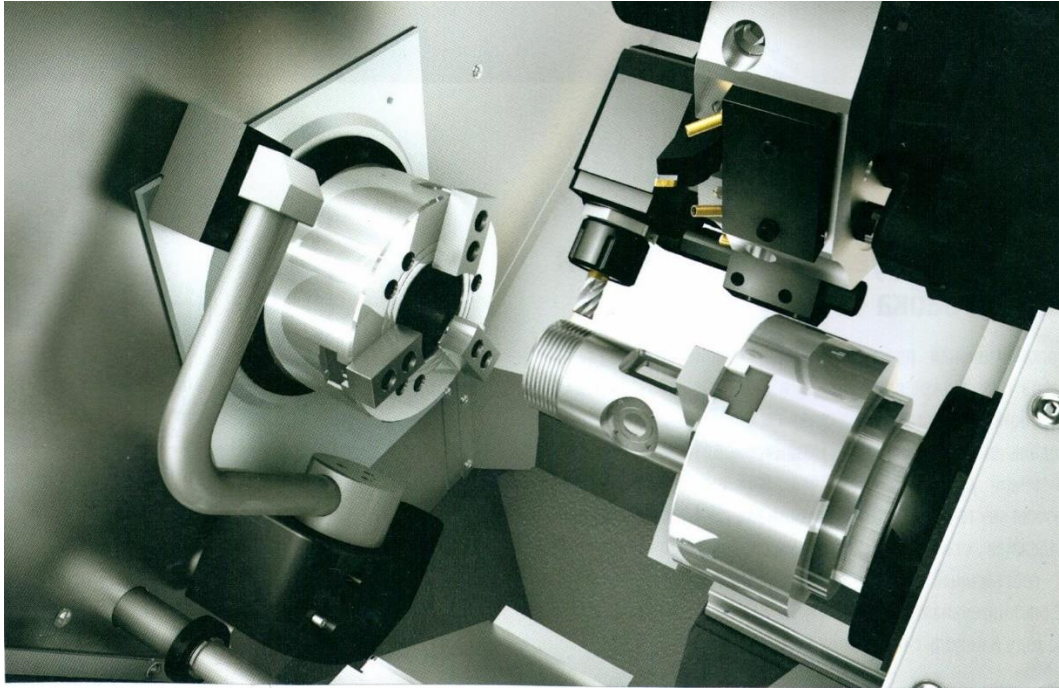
Обробка деталі за допомогою приводного інструмента
